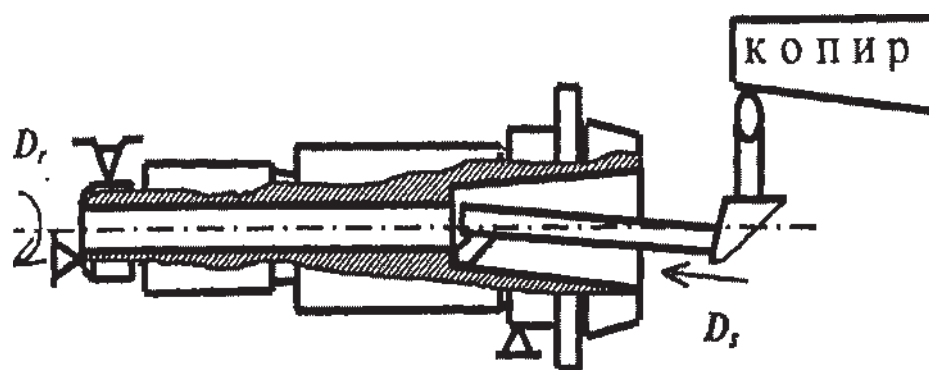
Схема обработки внутренних конических поверхностей на токарном станке с гидроконтрольным суппортом
